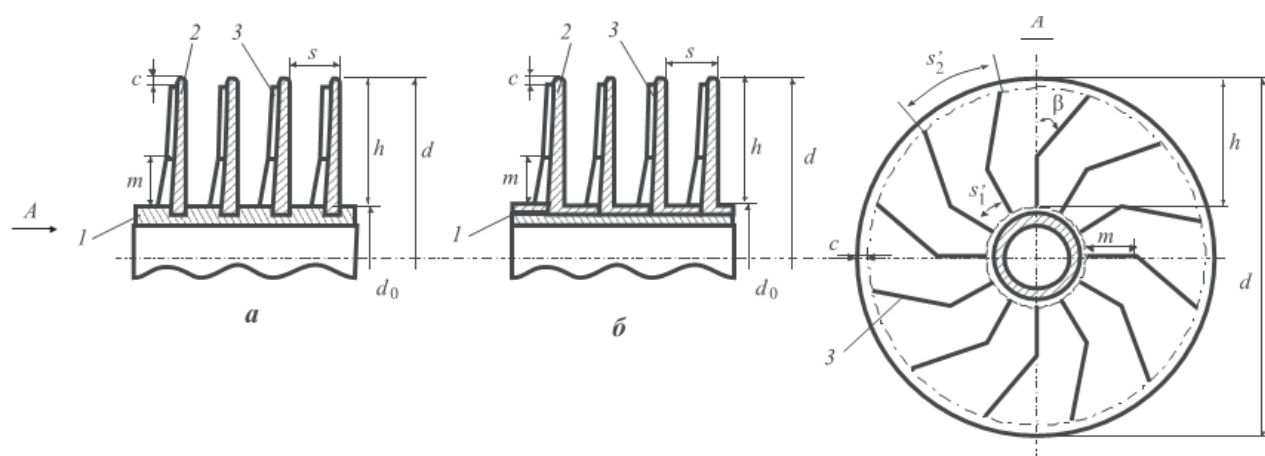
Труба с выступами, формирующими зигзагообразный рельеф [26]:
